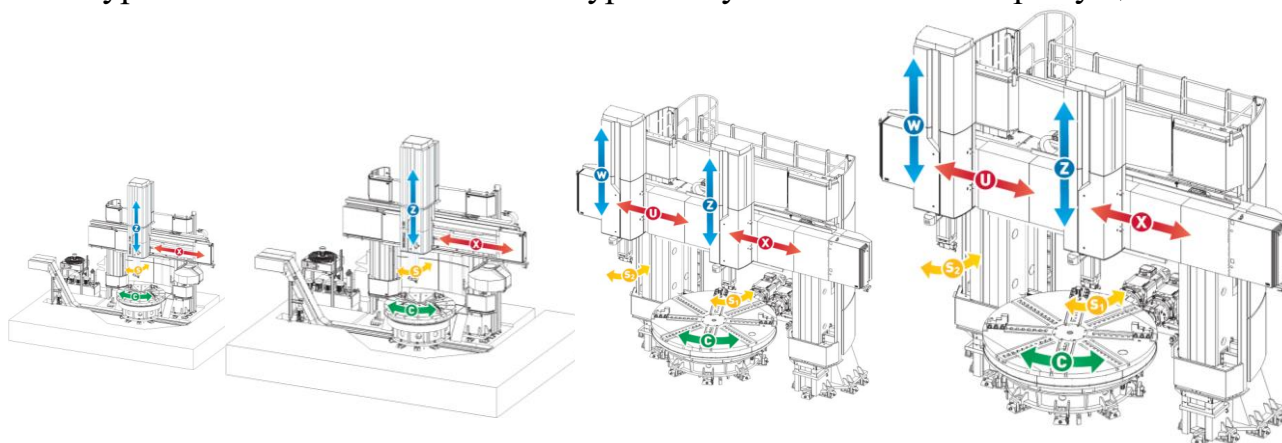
Типоразмерный ряд токарно-карусельных станков
